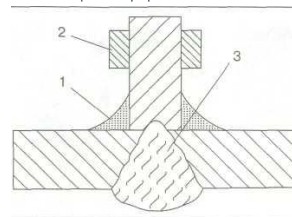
Схема паяно-зварного таврового з'єднання:
